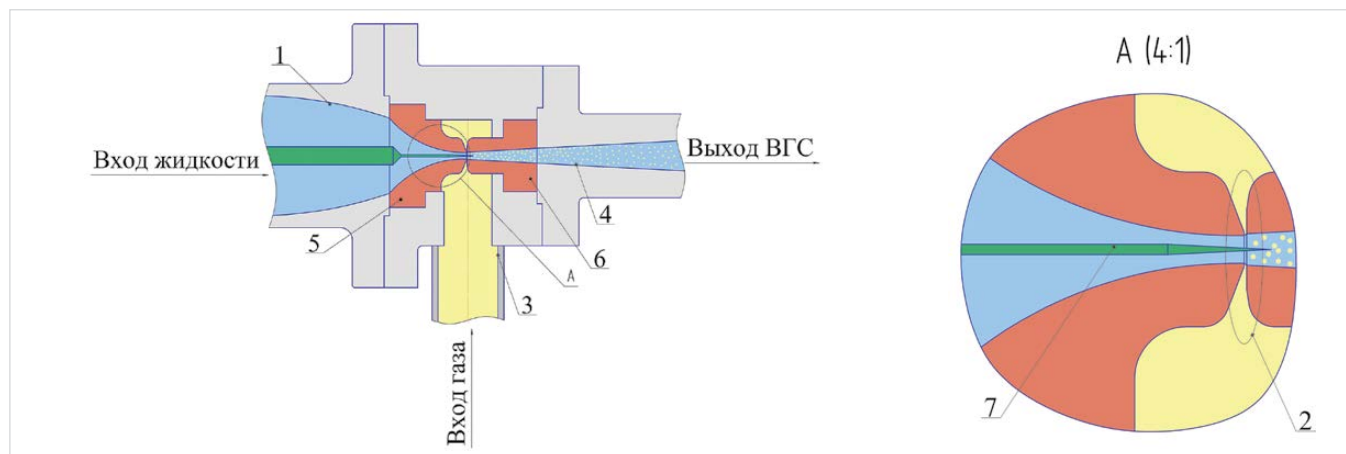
Конструкция эжектора с выдвигающейся конусной иглой Fig. 2 — Constructional design of the ejector with a retractable needle
